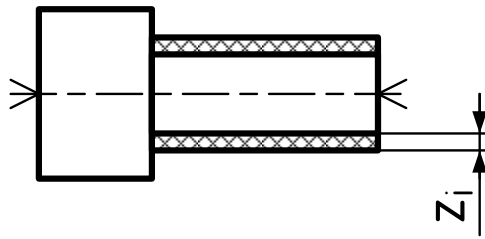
Припуск при обработке цилиндрической поверхности
